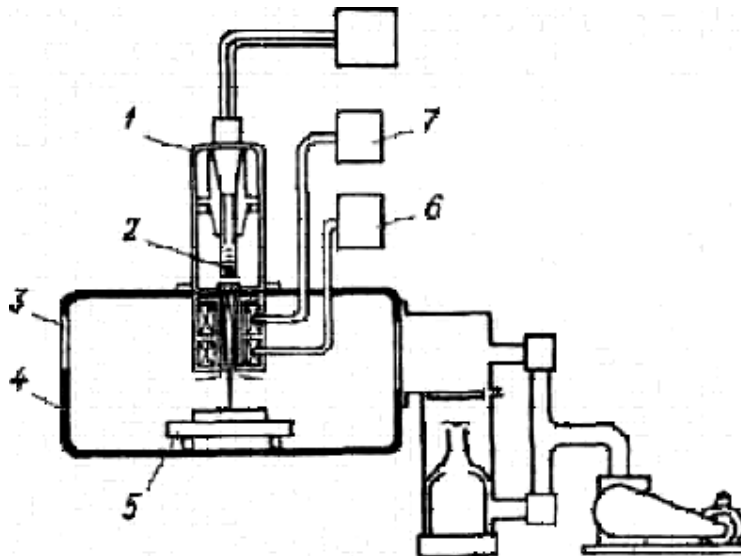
Схема установки для электронно-лучевой сварки
